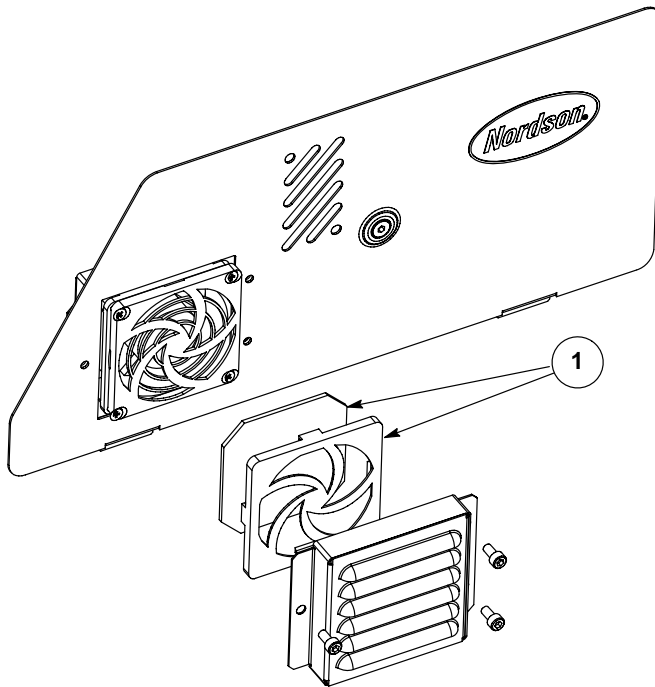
Ersatzteile Gebläsefilter Elektrogehäuse
